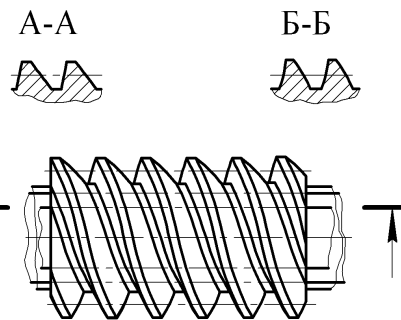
Эвольвентный цилиндрический спиroidный червяк – SZI
